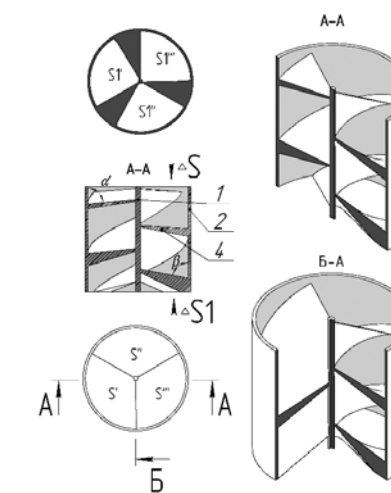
Турбіна з прямими спіралеподібними лопатями, які збільшуються в об'ємі (1 – вал, 2 – порожнистий циліндричний корпус, 3 – спіралеподібна лопать)
